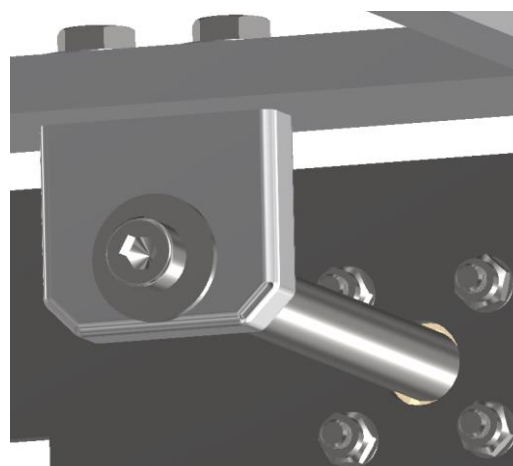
Uložení pneumatického válce bočního přítlačného mechanismu
